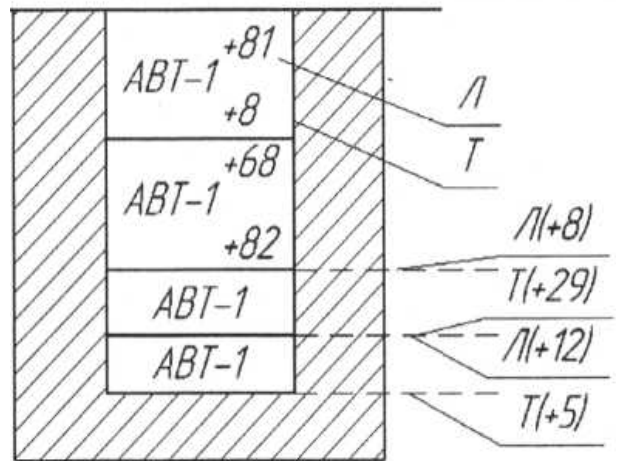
Схема компоновки из четырех образцов из алюминиевого сплава АВТ-1
